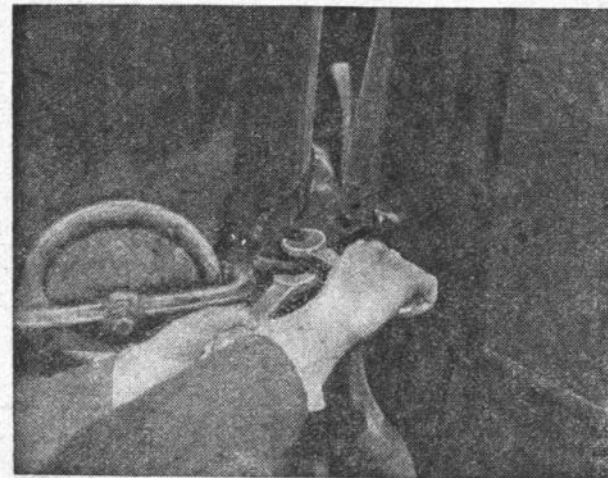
Проверка и подтяжка болтовых креплений газогенераторной установки.
